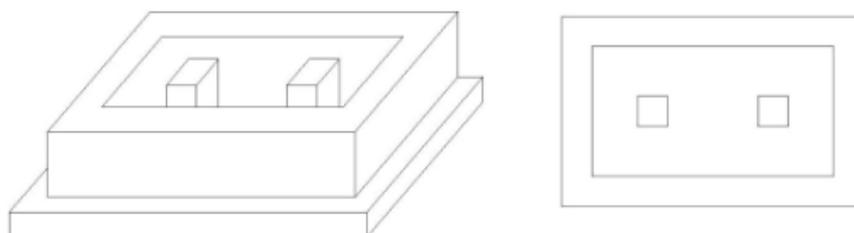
Detalle en elevación y planta de molde para Eco-ladrillos de Concreto
